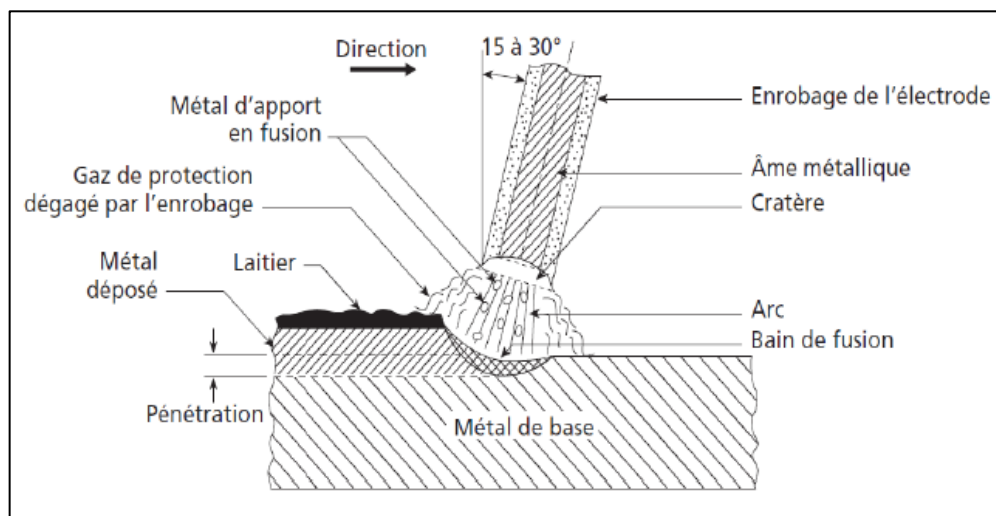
Principe de soudage à l'arc avec électrode enrobée (SMAW). [4]
